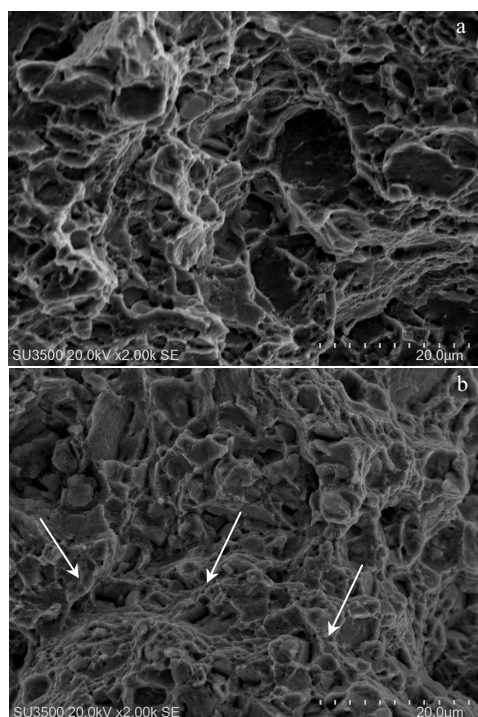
GH720Li 合金裂纹扩展区断口形貌
